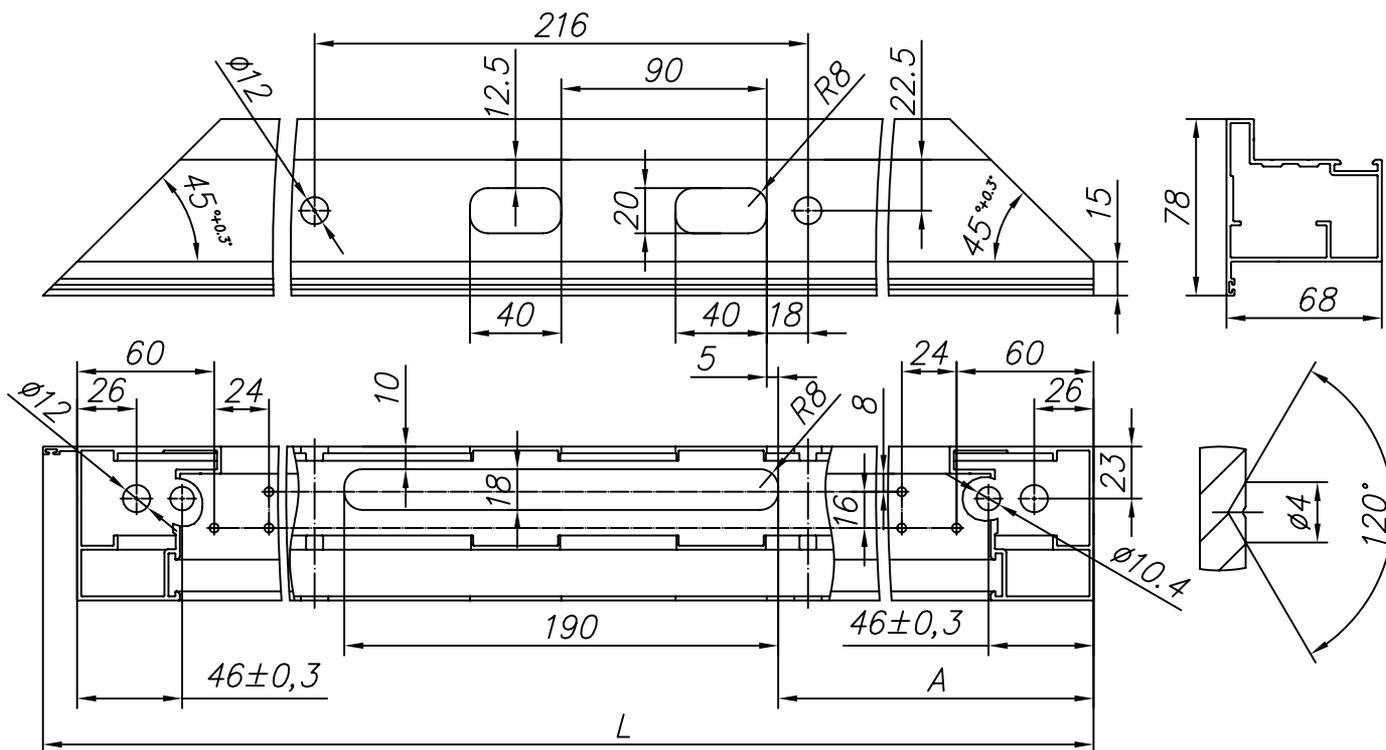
Изготовление стойки с пазом для замка из профиля FLGU.400.0108 (калитка с перекладиной, открывание наружу, влево)
